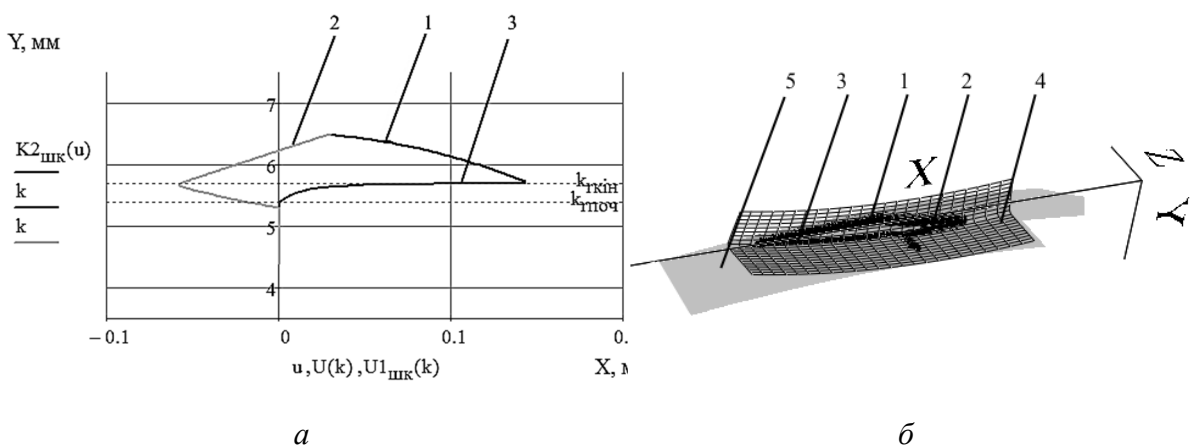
Пляма контакту фрези й кулачка розподільного вала при обробці ділянки кулачка найбільшого радіуса
